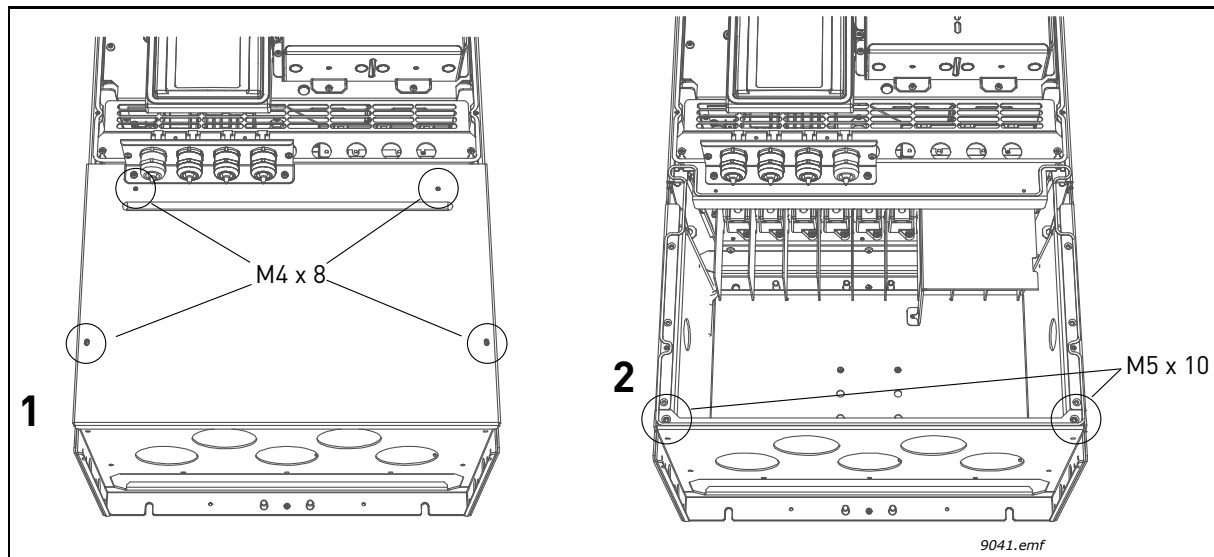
Снятие крышки кабельного отсека и кабельной планки (MR9).
